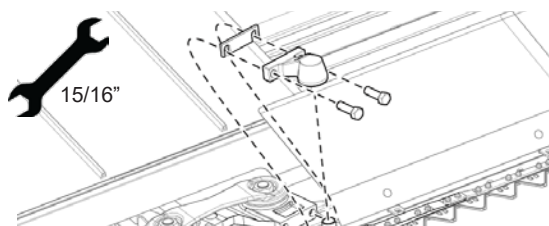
Снятие корпуса подшипников с головки левого ножа
